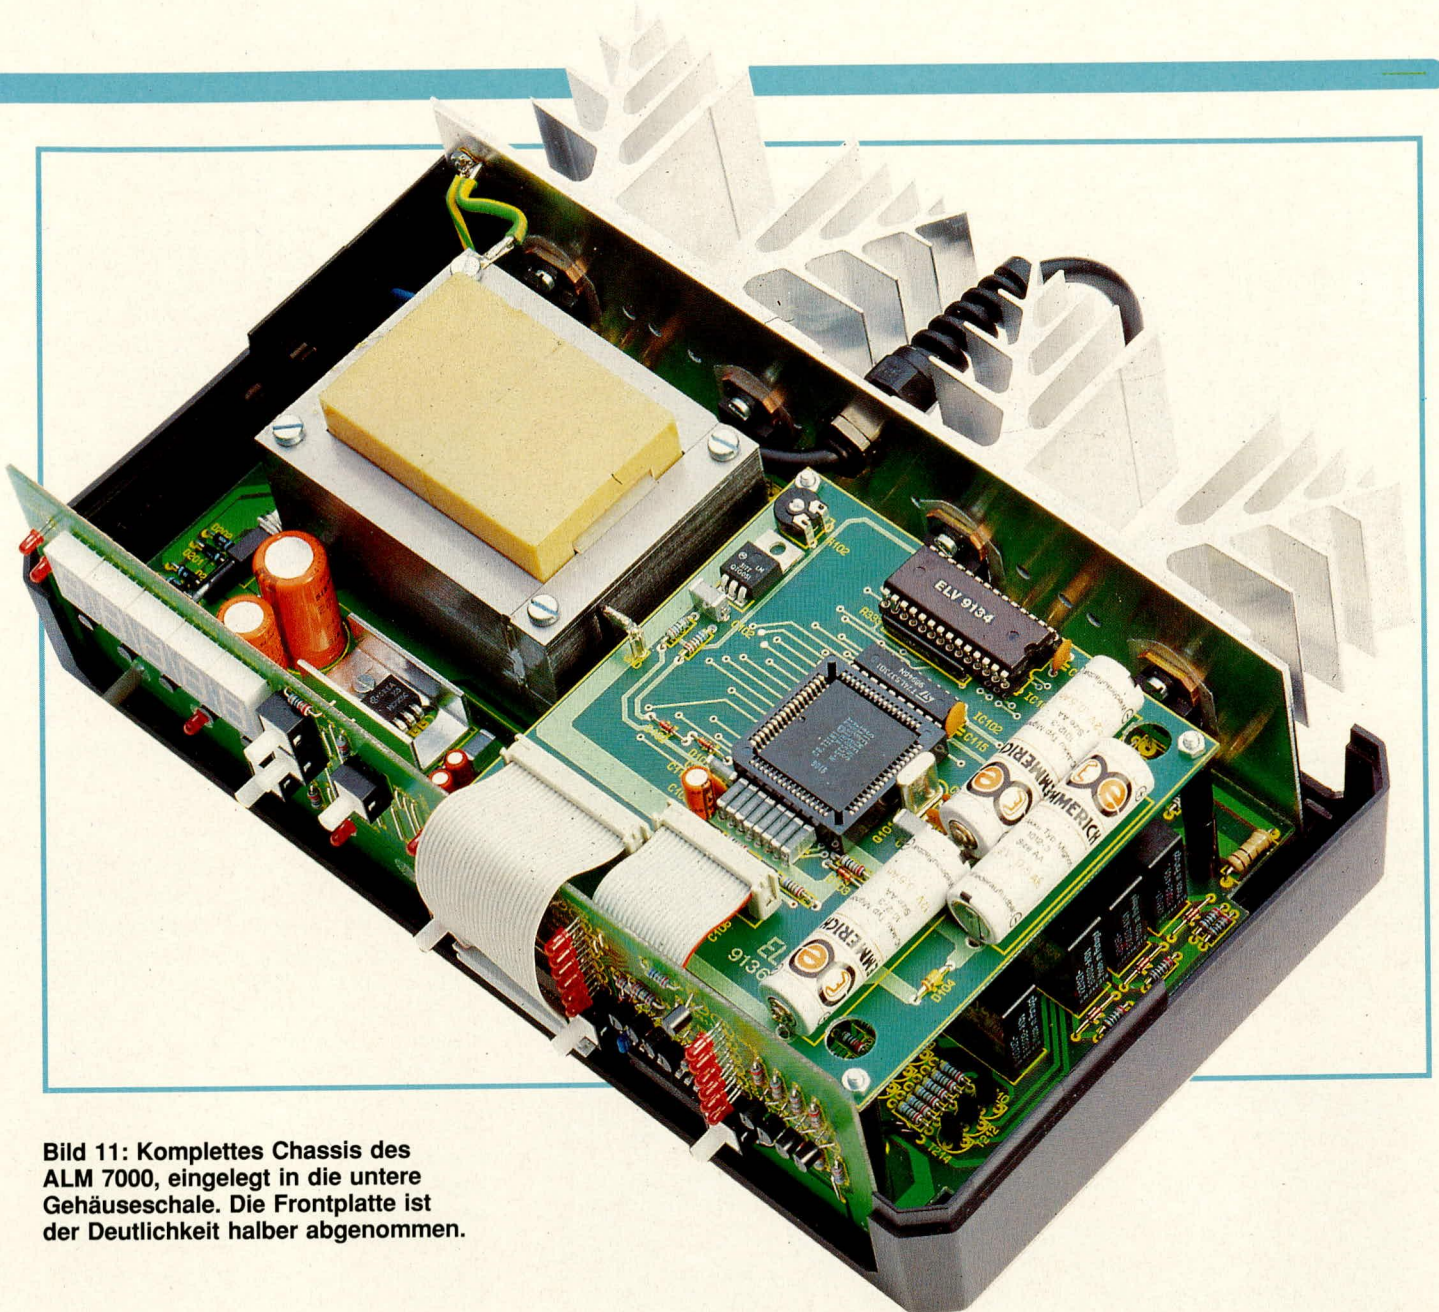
Komplettes Chassis des ALM 7000, eingelegt in die untere Gehäuseschale. Die Frontplatte ist der Deutlichkeit halber abgenommen.
